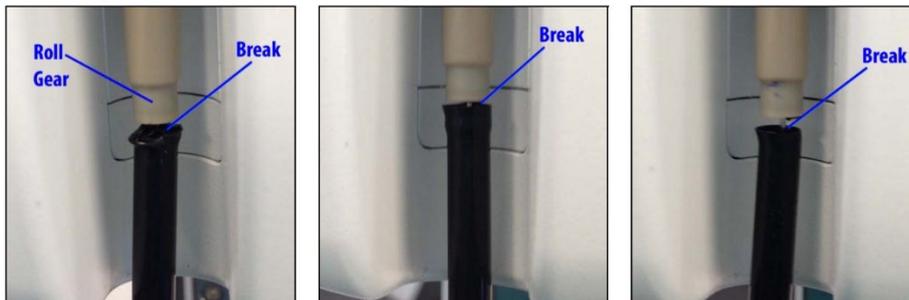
roll gear 및 instrument shaft 접합부의 brake 의 예
